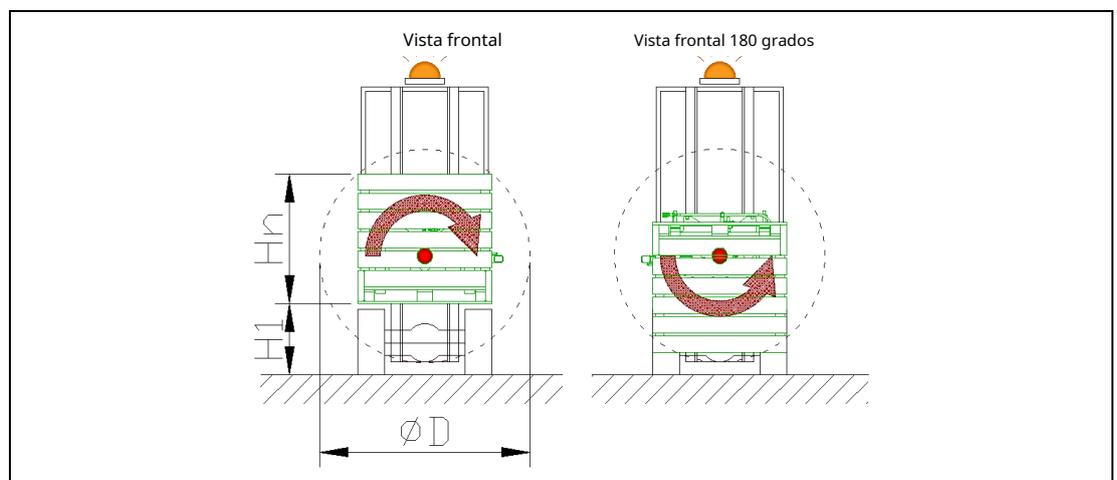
Zona de trabajo de la carretilla elevadora con plato giratorio - vista frontal
